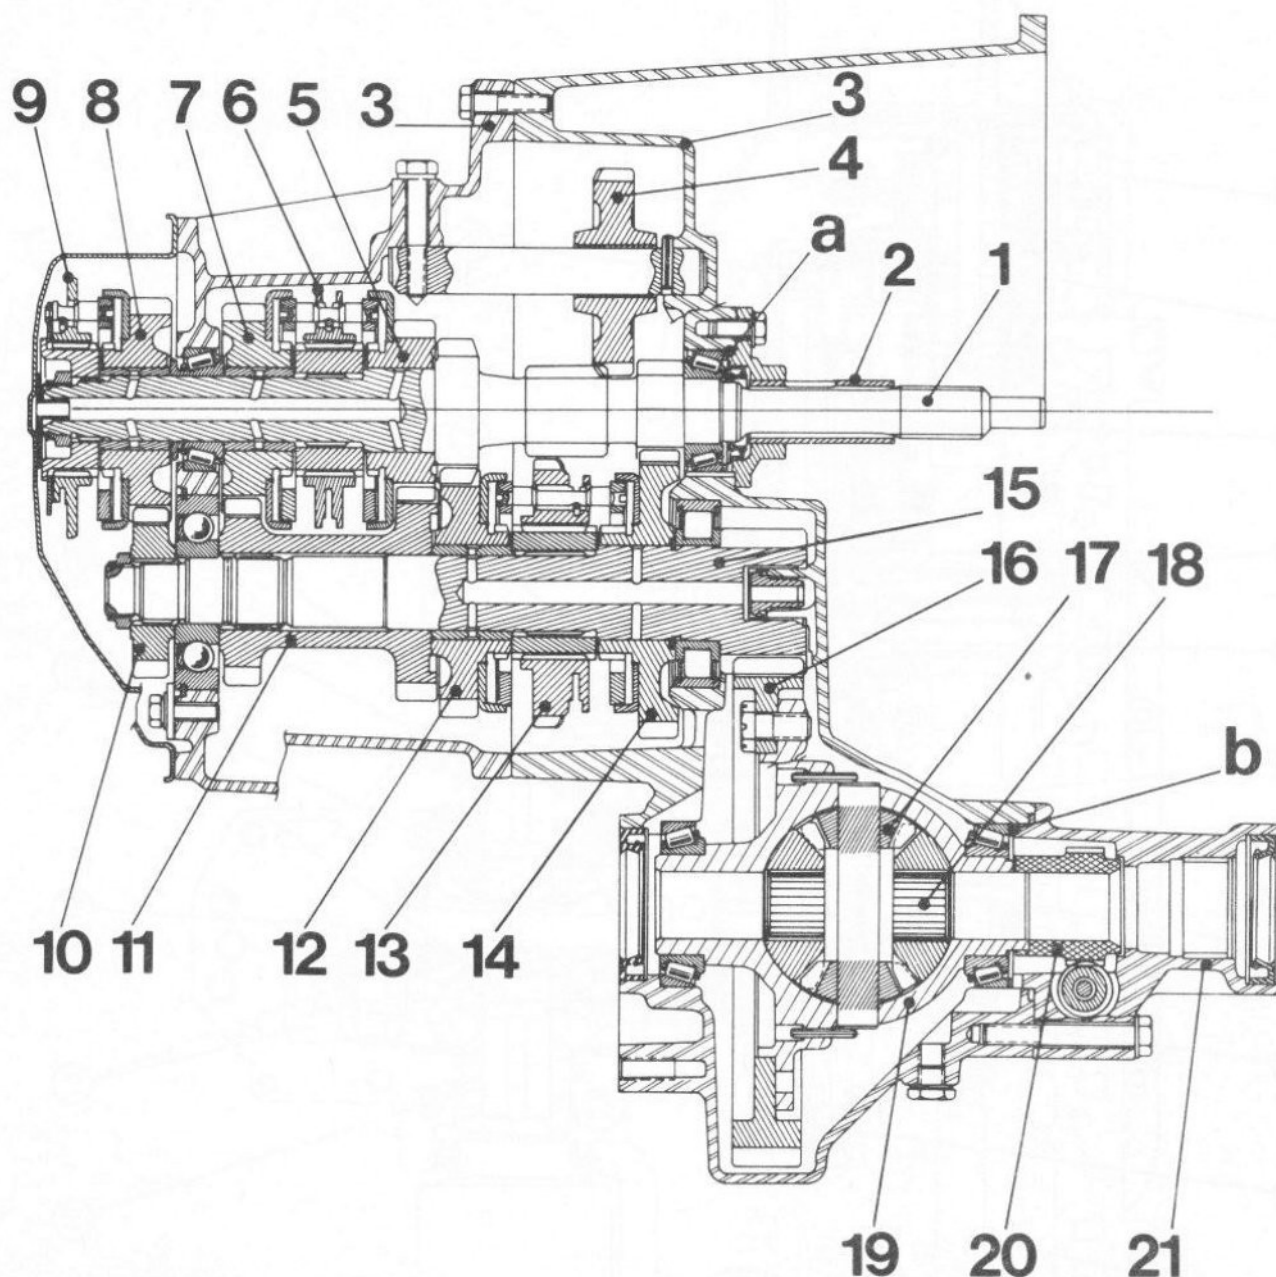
Coupe de la boîte BE 1/5 (Sec 1)
